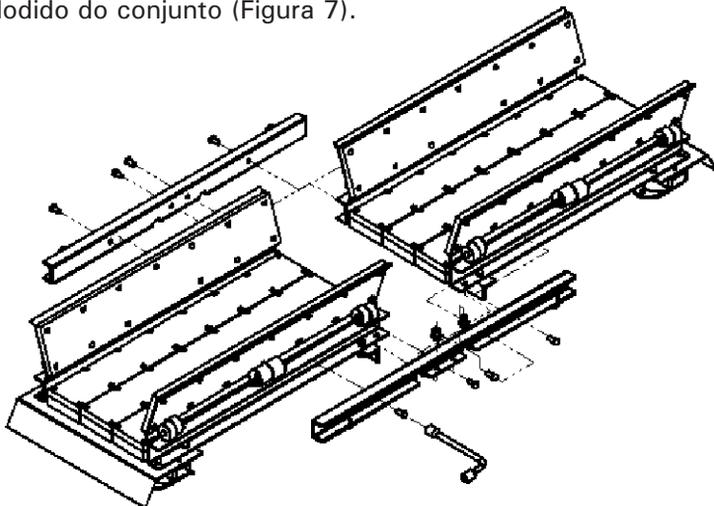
Conjunto de peças que compõem a plataforma regulável de pesagem.
